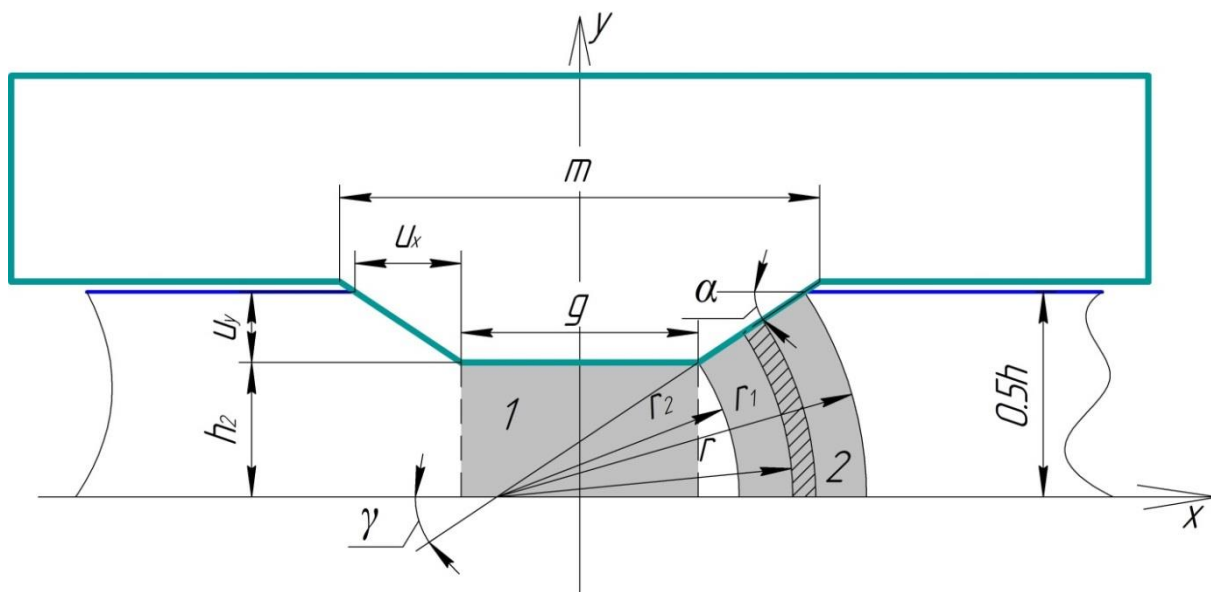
Внедрение трапециевидного выступа в заготовку
